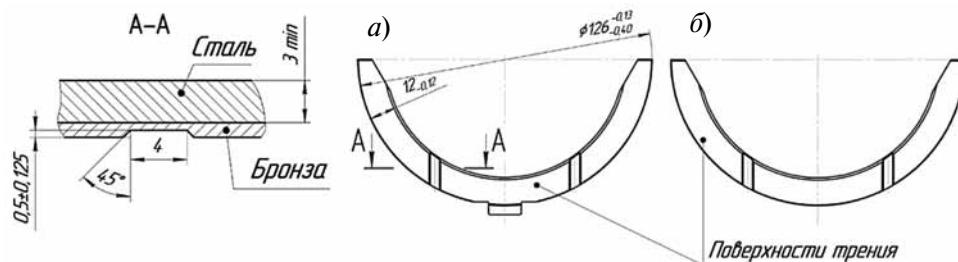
Конструкция серийных нижнего и верхнего полуколец осевых подшипников коленчатого вала:
